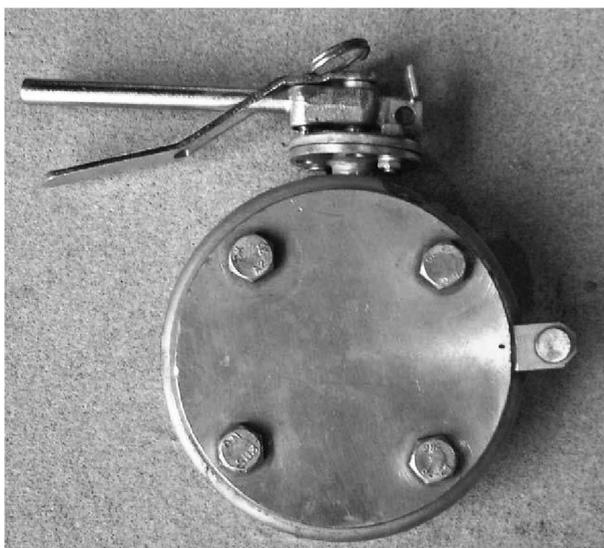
Типичный верхний выпускной клапан «бабочка» с фланцем
